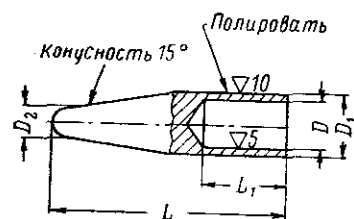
Типовая конструкция конусной оправки для установки фторопластовых шайб в наружные канавки деталей
